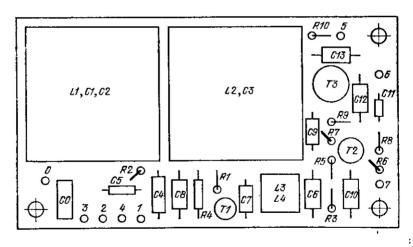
Монтажная схема платы второго смесителя (вид сверху)
